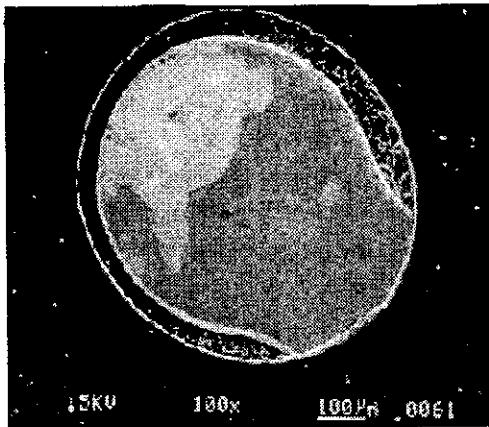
SEM micrograph, showing solder de-wetting, on the pad
